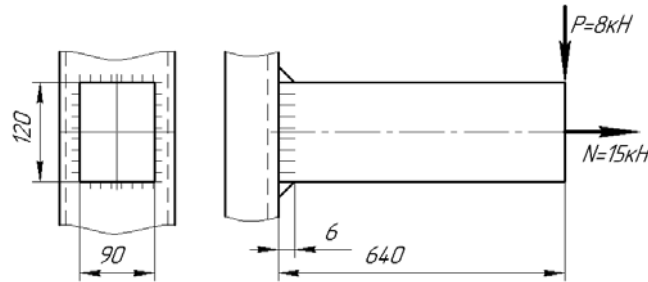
Сварное соединение бруска со швеллером
